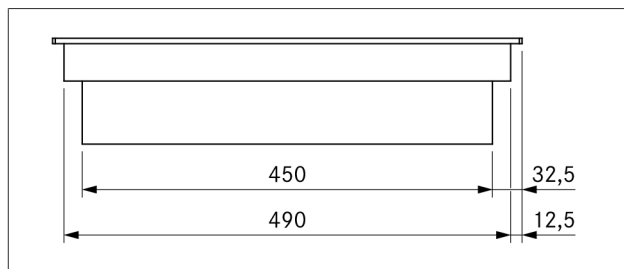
Dimensões do aparelho CKIW, vista lateral
